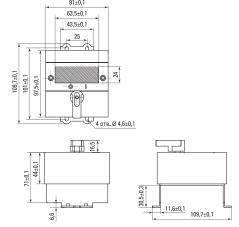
Габаритные размеры моторного привода к ВА-99М 100
